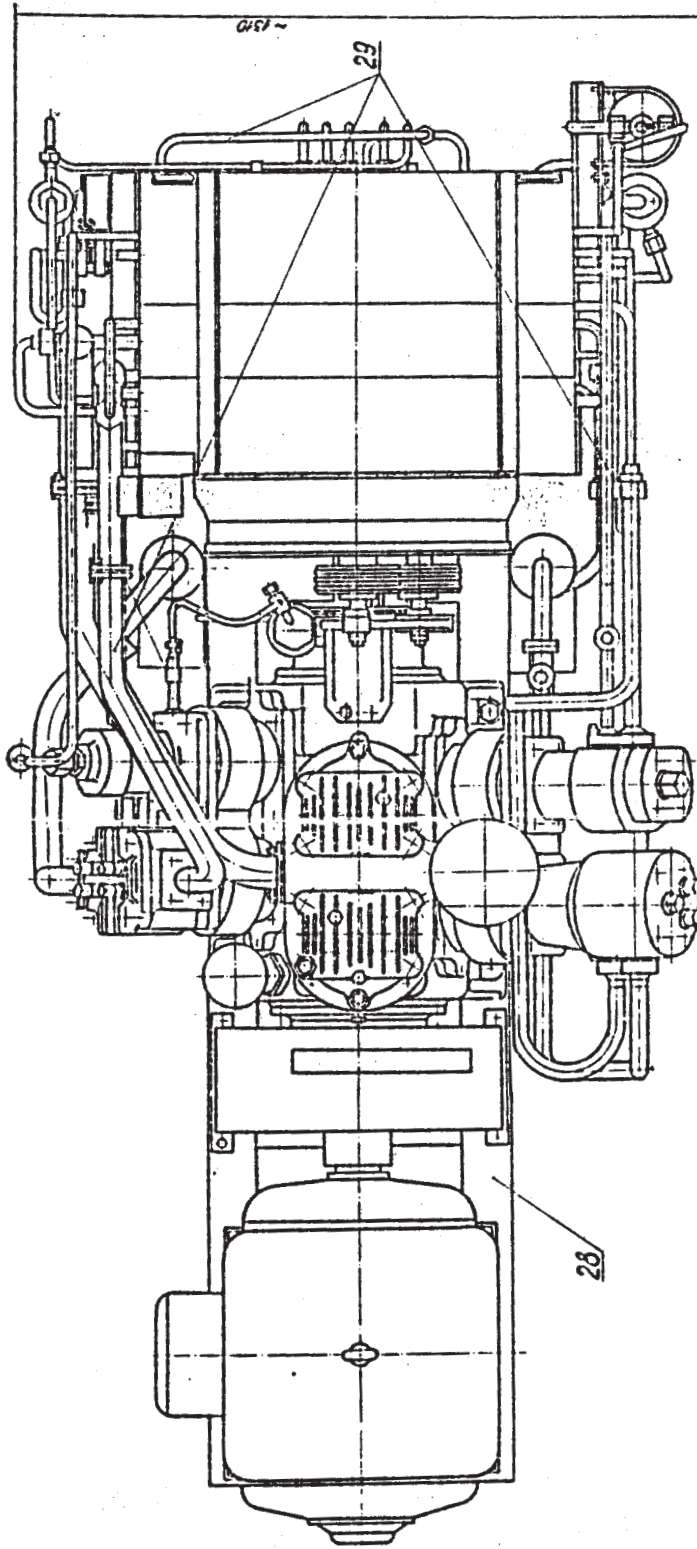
Компрессор с приводом электродвигателя, механизм качения компрессора и детали: 28 - корпус, 29 - детали компрессора.
